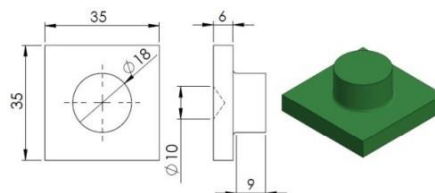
Desenho base para a usinagem dos corpos de prova utilizados nos ensaios.
